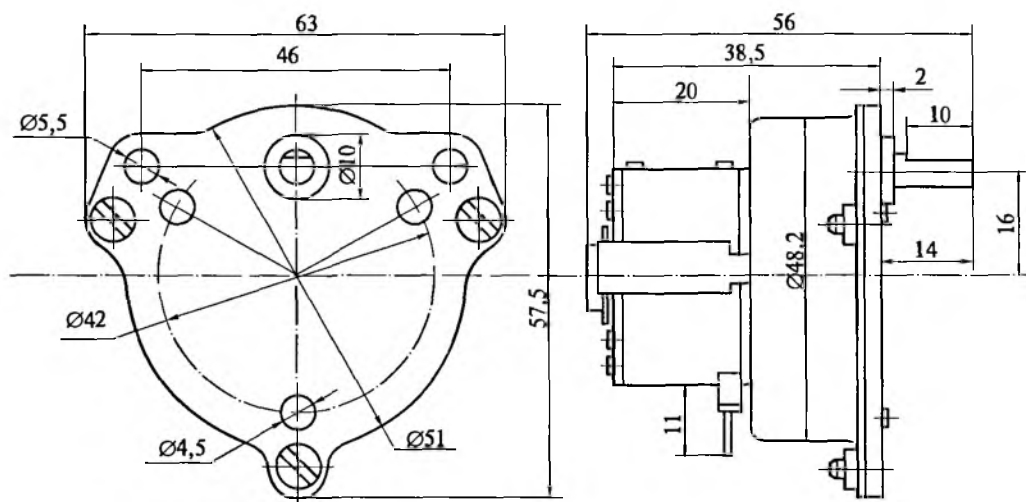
Габаритные и установочно-присоединительные размеры синхронного редукторного двигателя ДСОР-32
